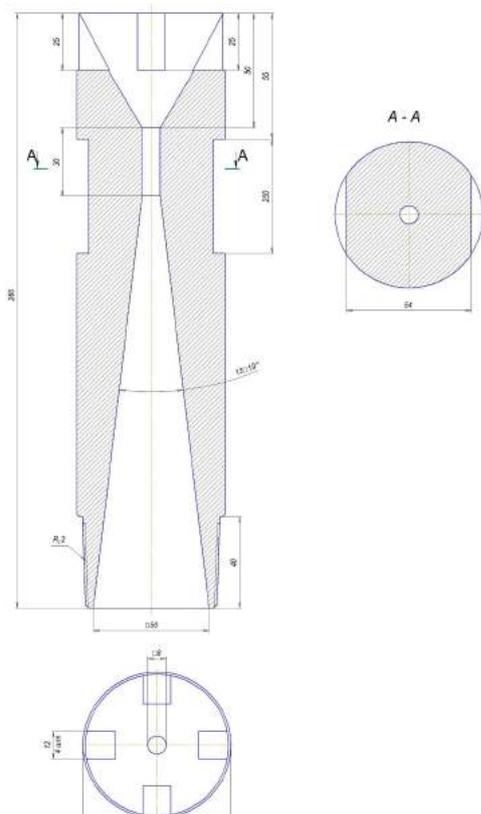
Гидродинамическое устройство для скважин с обсадной колонной Ж
